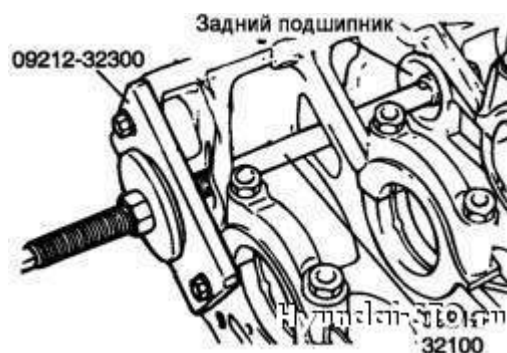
(#) Demontáž pravé přední ložisko vyvažovací hřídel
